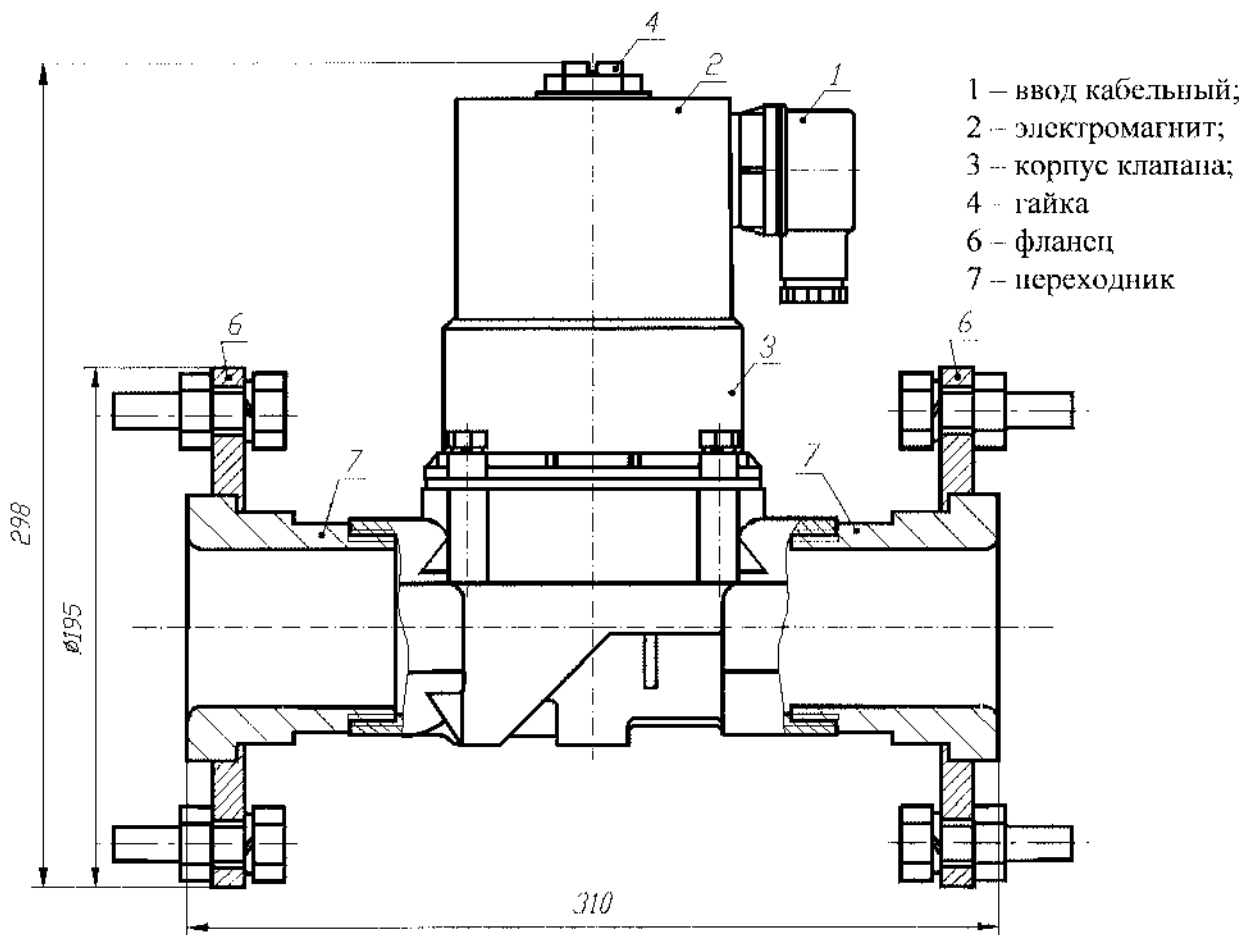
Габаритные и установочные размеры клапана КГЭЗ-65
